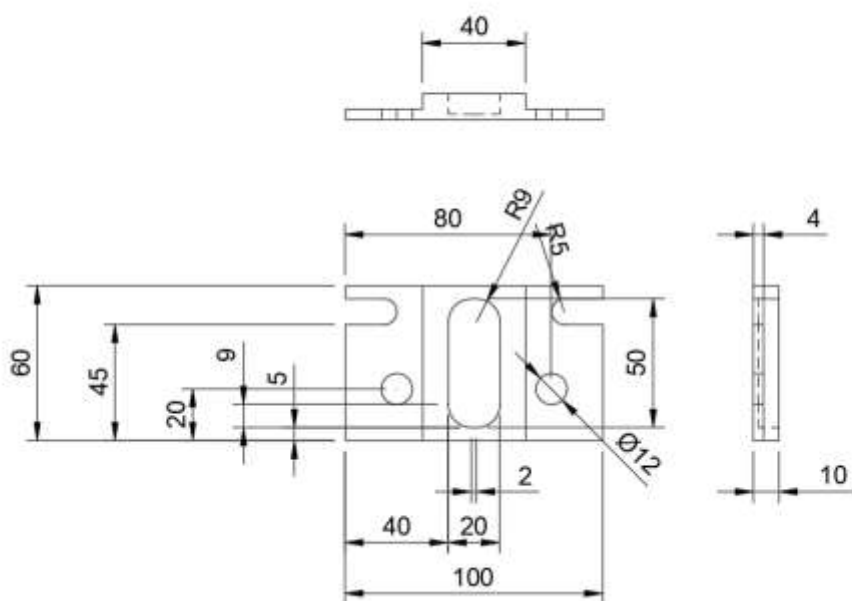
Чертеж детали, созданный в ПО Fusion 360
